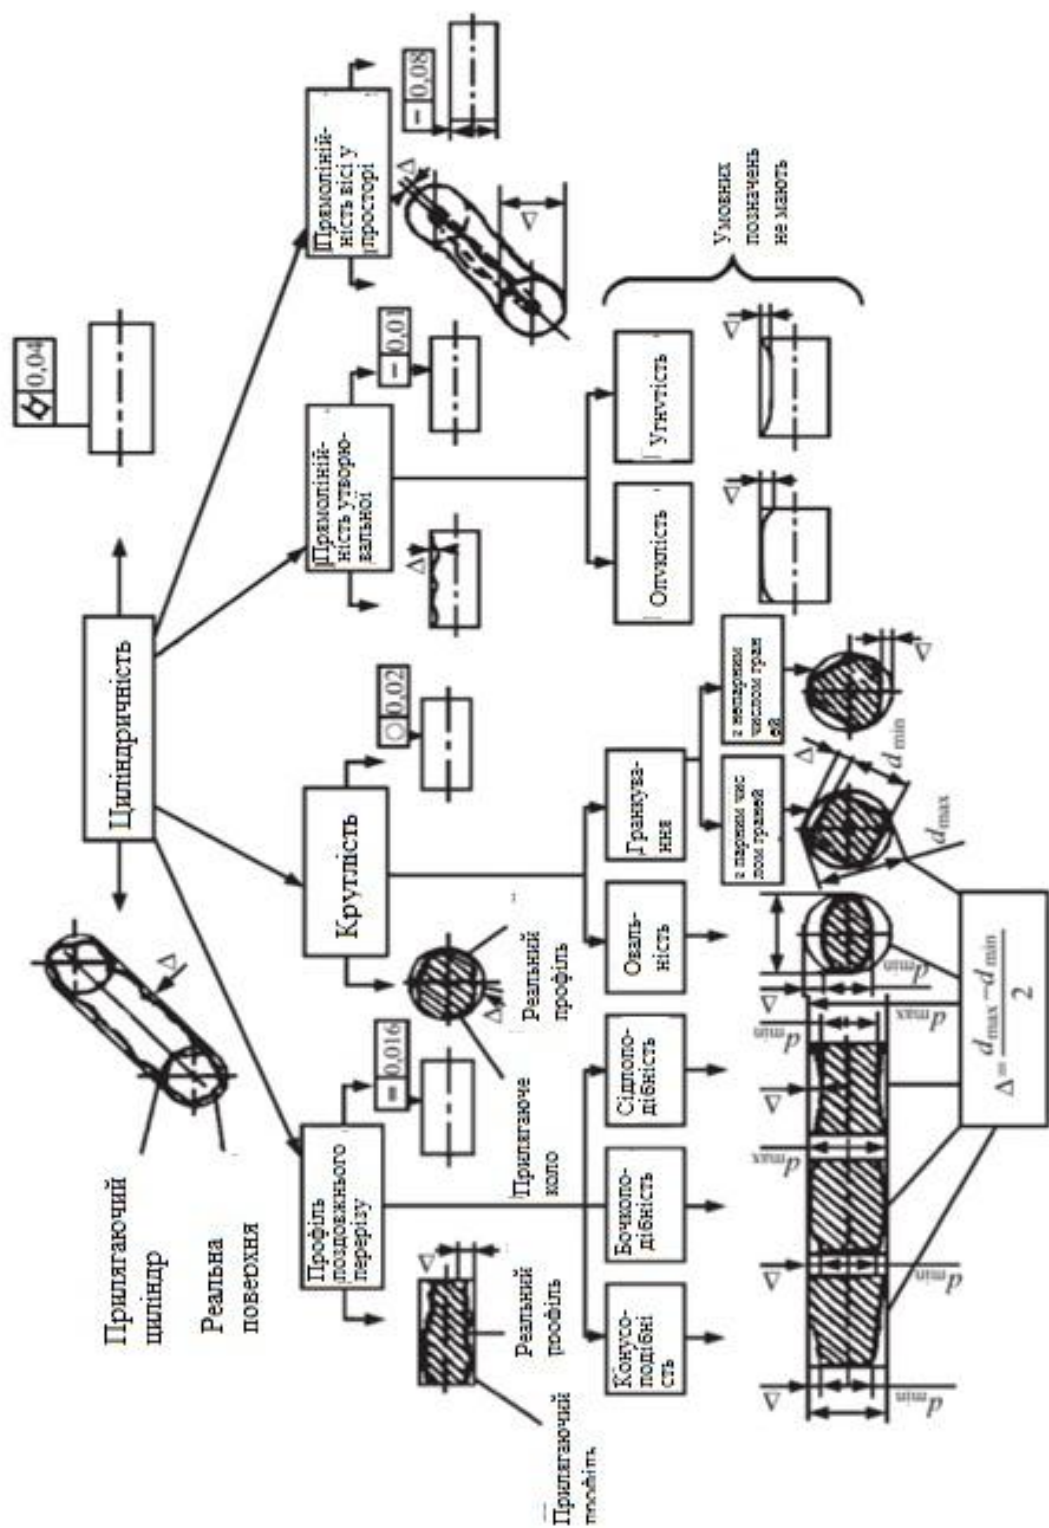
Види відхилень циліндричних поверхонь
